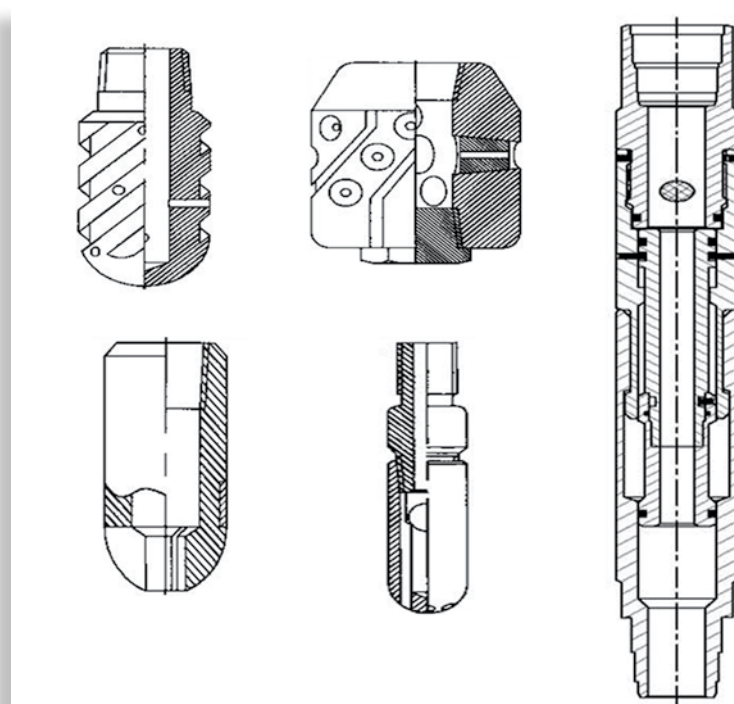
Примеры конструкций промывочных насадок и гидравлического разъединителя
